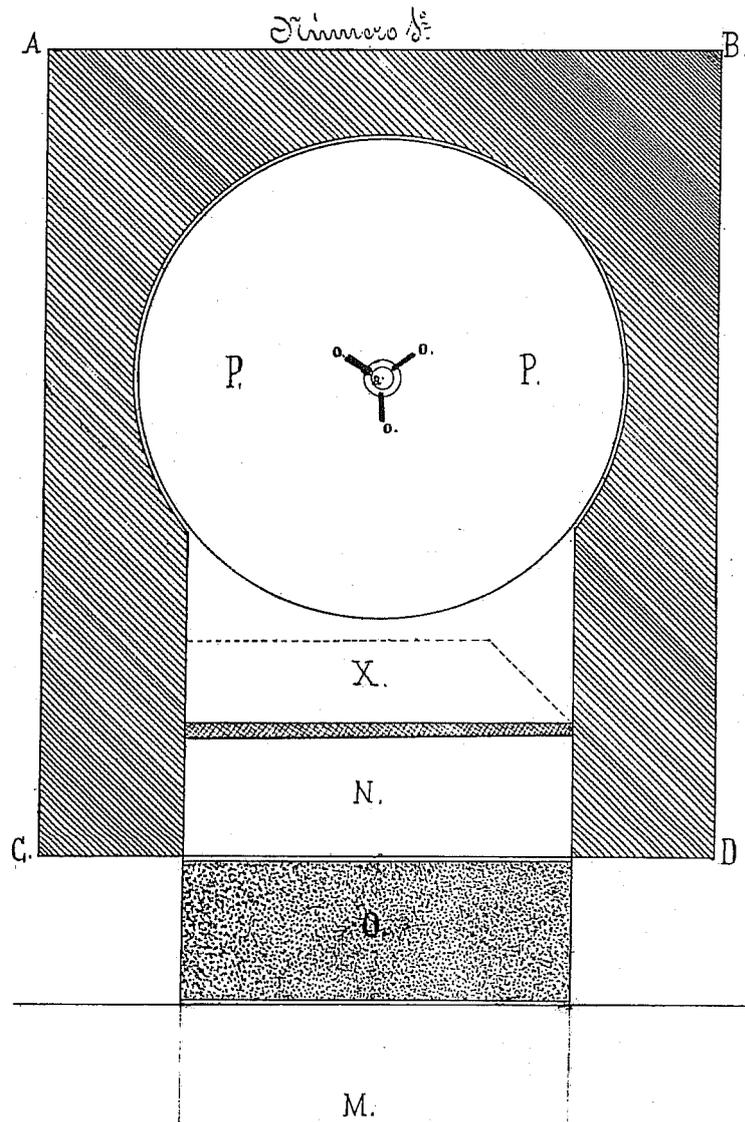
Planta del Flotador Salmerón. Plano Número 1, original de la patente.
